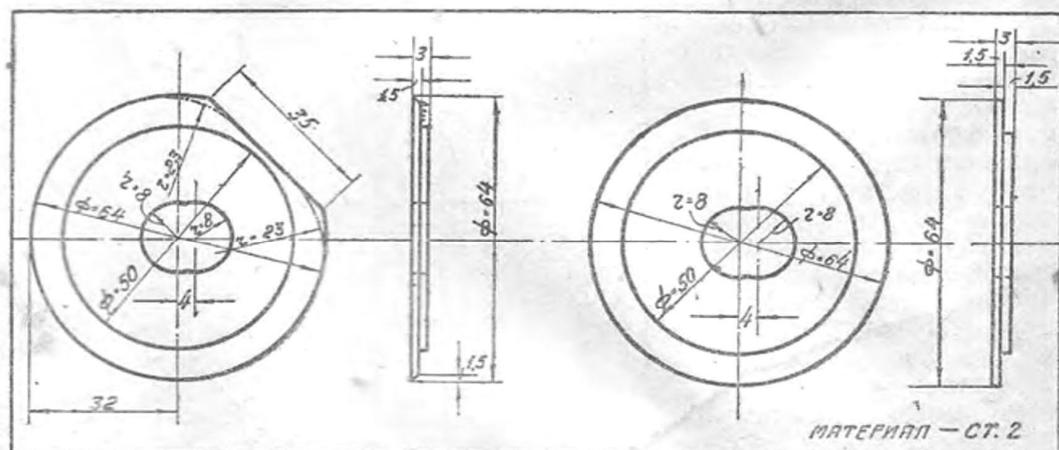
Шайбы головок: поворачивающейся (слева) и неподвижной (справа) стоек механизма автомата для смены пластинон.
